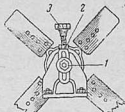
Регулировка натяжения ремня вентилятора ЗИС-5
